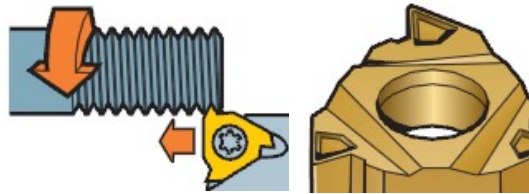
Інструмент для нарізування зовнішньої різьблення
